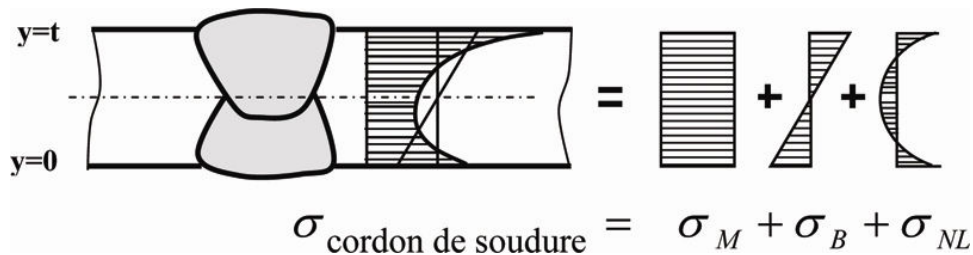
Définitions des contraintes au voisinage d'un cordon de soudure [1-1]
